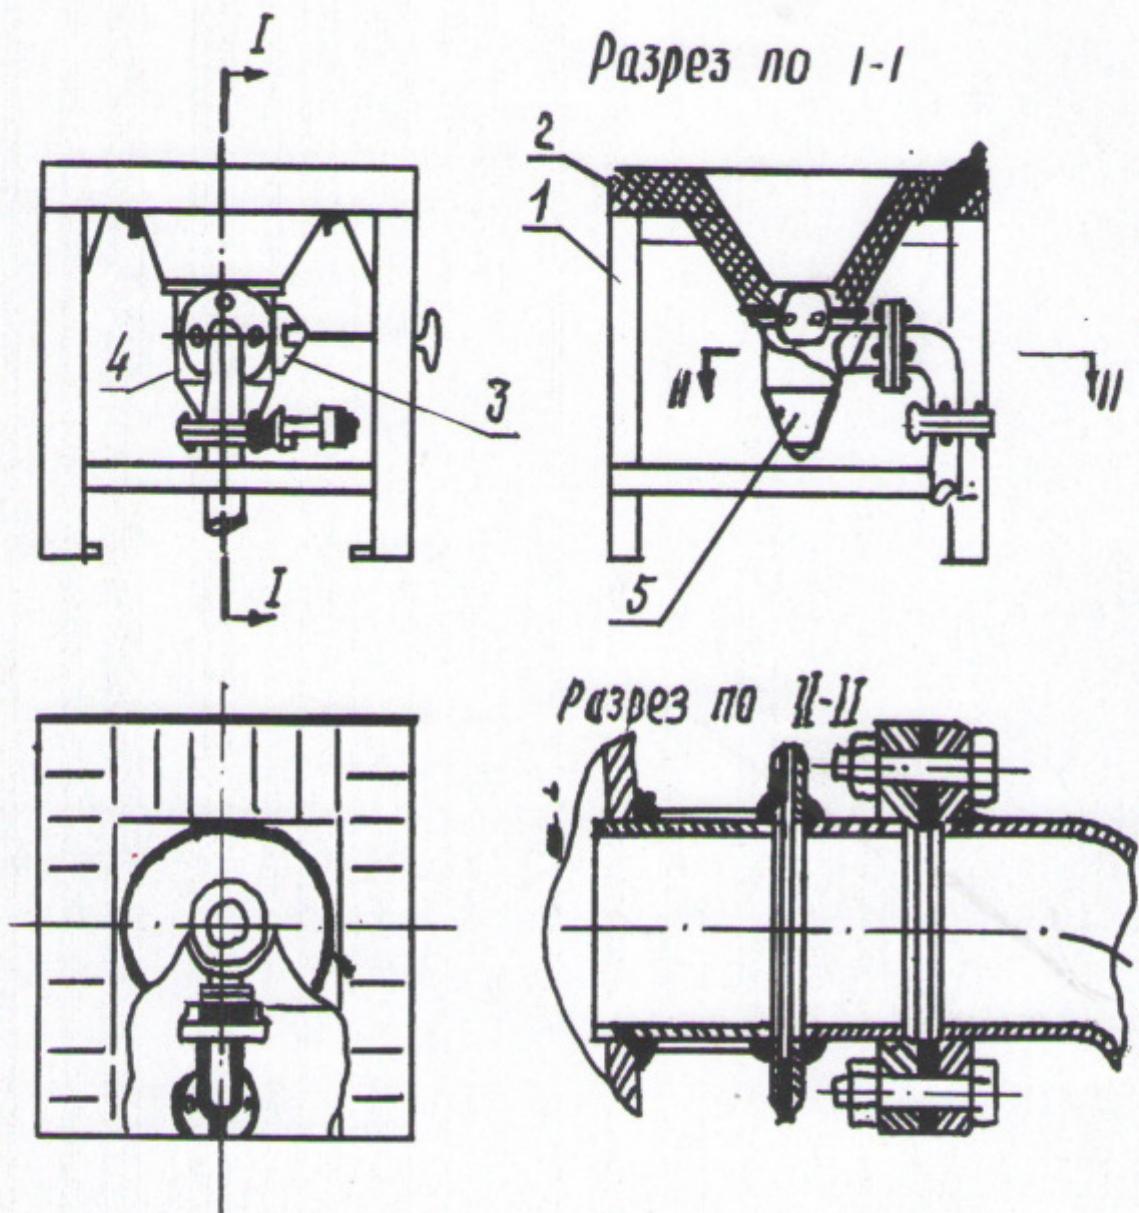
Кузнечный горн сварной конструкции на один огонь:
